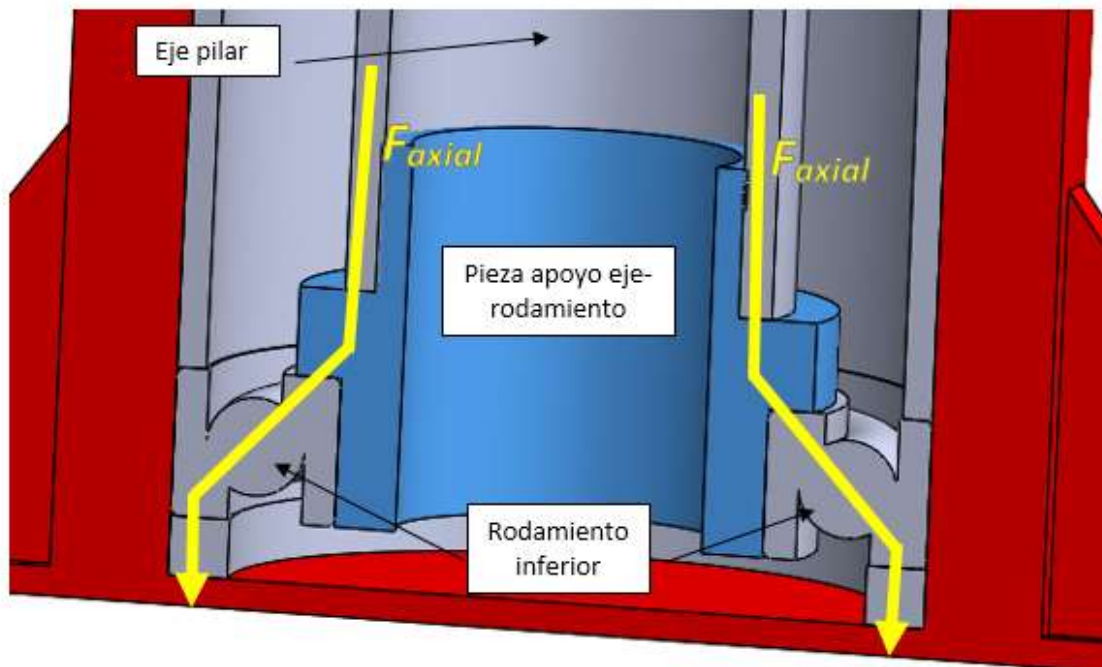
Función de la pieza para la transmisión de fuerza axial.
